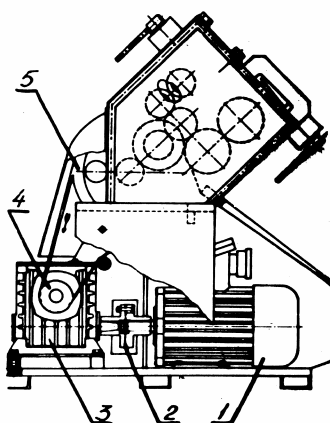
Двухклетьевого прокатный стан СПЦД-6
